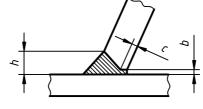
Préparation et ajustage des bords à souder — Soudures d'angle dans des assemblages entretoise-membrure à profils creux circulaires
